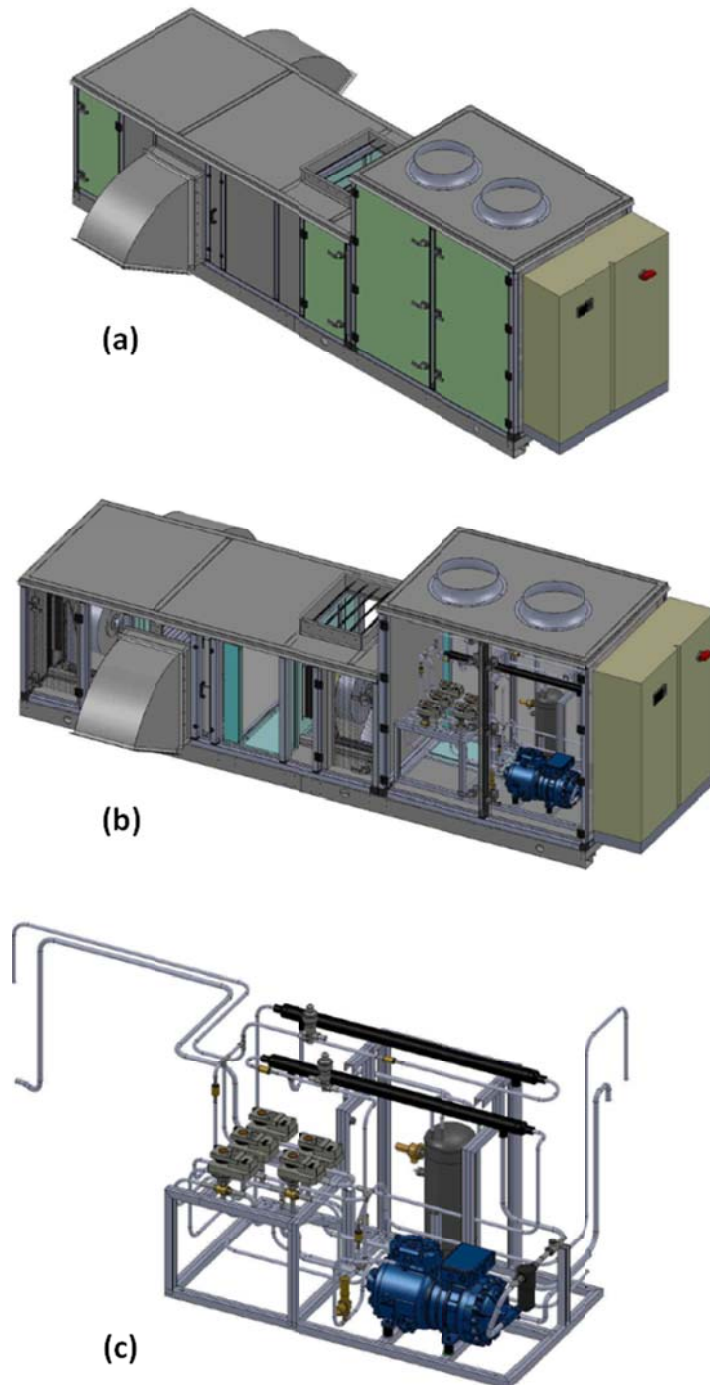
(a) Vista tridimensionale del roof-top, (b) vista tridimensionale in trasparenza, (c) particolare del circuito
